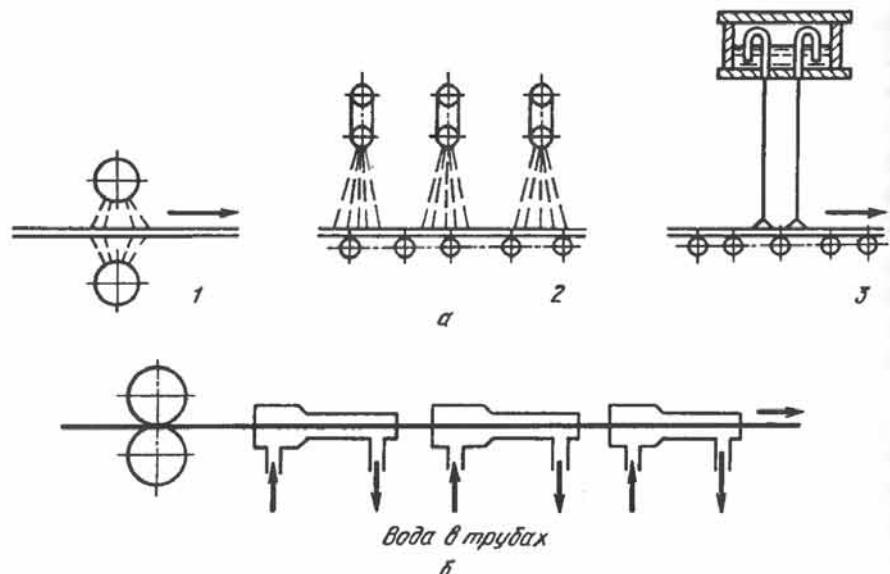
Схема ускоренного охлаждения листового проката (а) и катанки (б):
